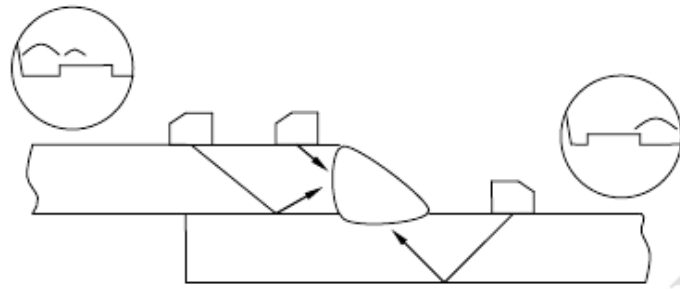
Схема контроля нахлесточных сварных соединений
